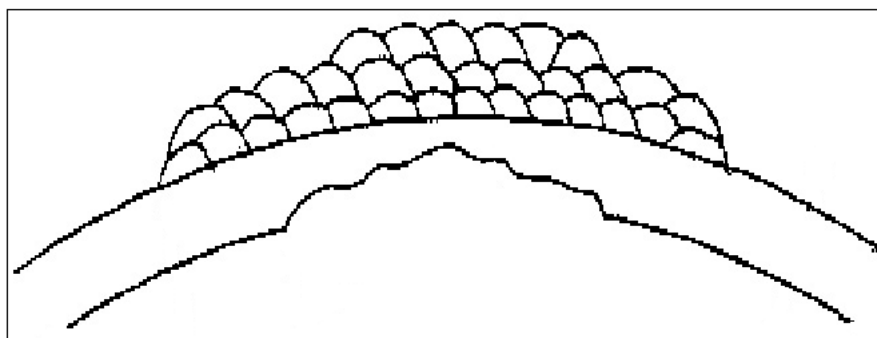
Solda de simples deposição sobre tubo com perda de parede interna [22].
